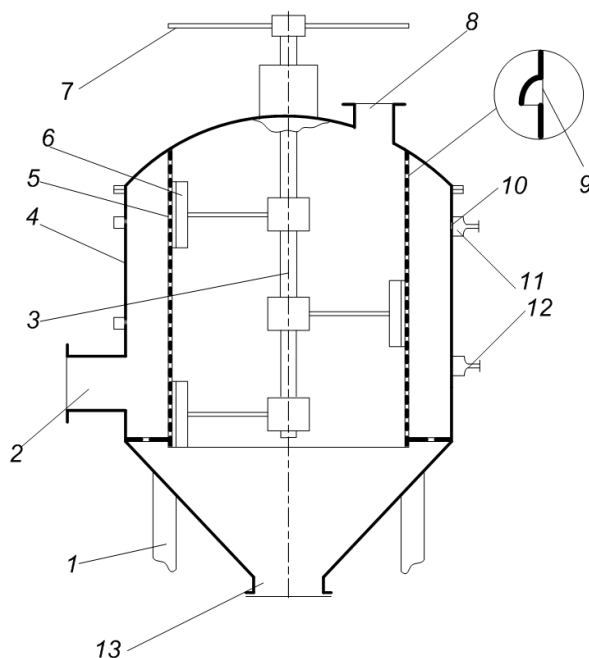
Конструкция аппарата-ловушки: 1 – рама; 2, 8, 12, 13 – штуцеры; 3 – вал; 4 – наружный корпус; 5 – перфорированный внутренний корпус; 6 – скребок; 7 – привод; 9 – вид перфорации; 10 – отверстия для промывки; 11 – кольцевой промывной канал
